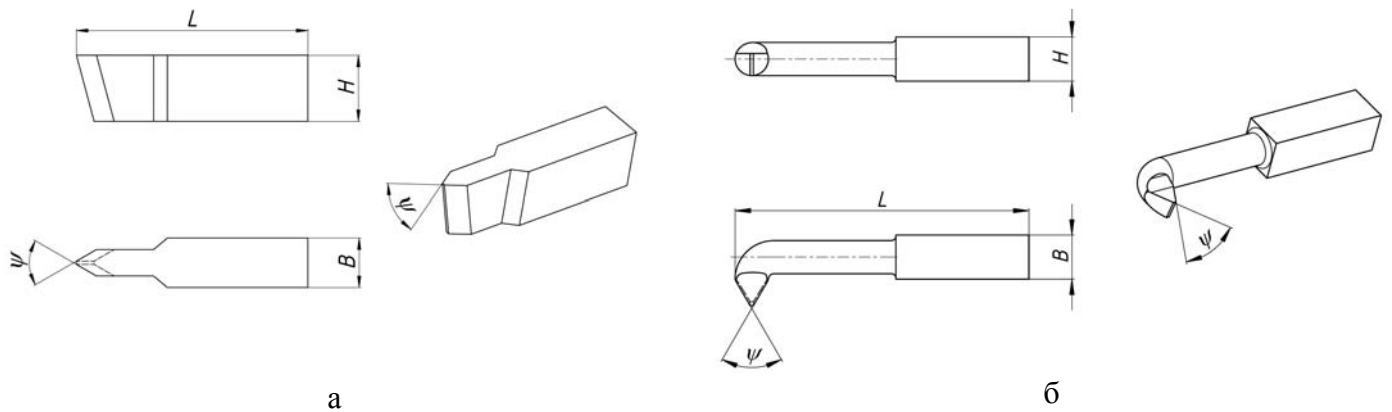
Резьбовой стержневой резец: а) для наружных резьб; б) для внутренних резьб
